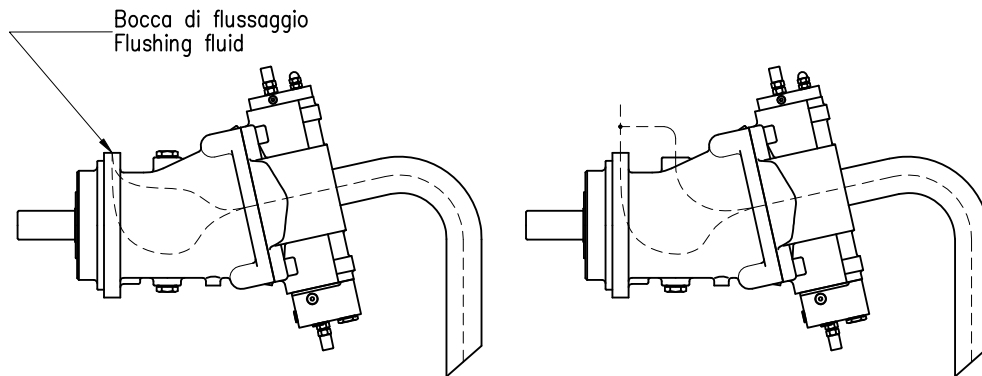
Flussaggio cuscinetti / Figure 4 - Bearings flushing
